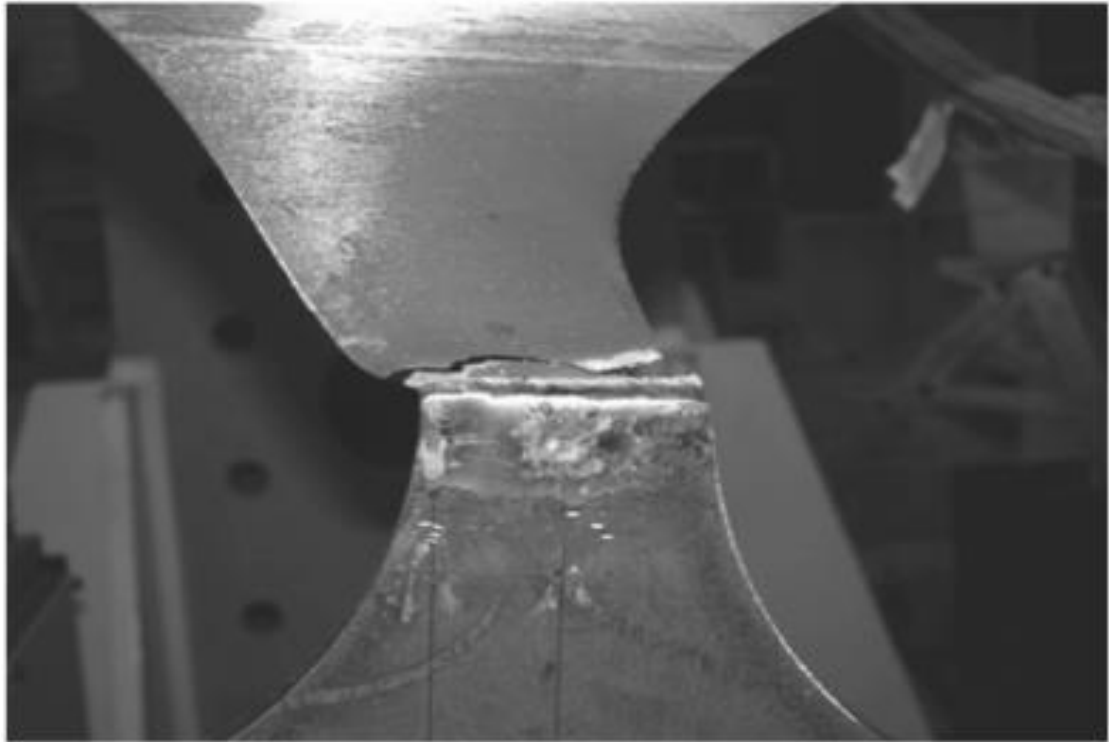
Fallo por ruptura cordón de soldadura
